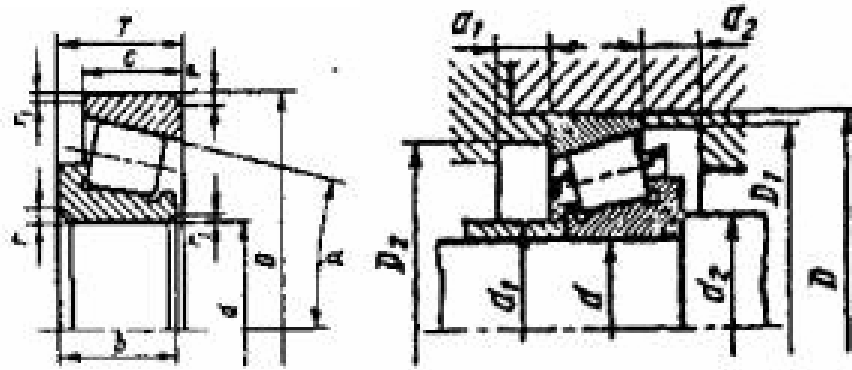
Підшипник роликовий конічний радіально-упорний однорядний
